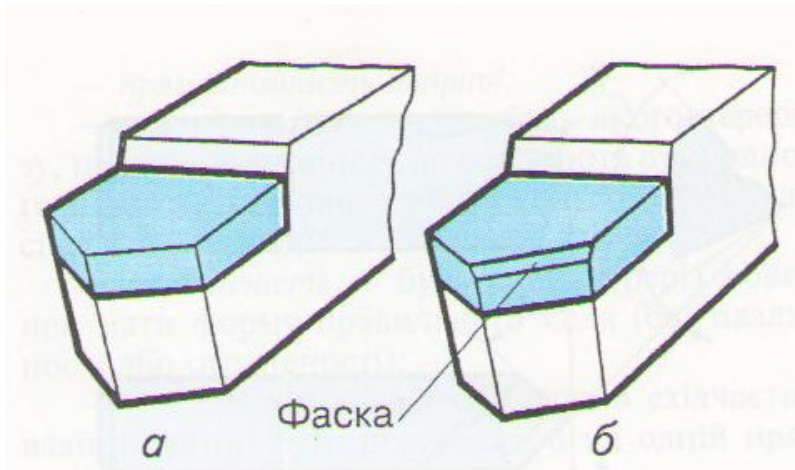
Форми передньої поверхні твердосплавного різця:
